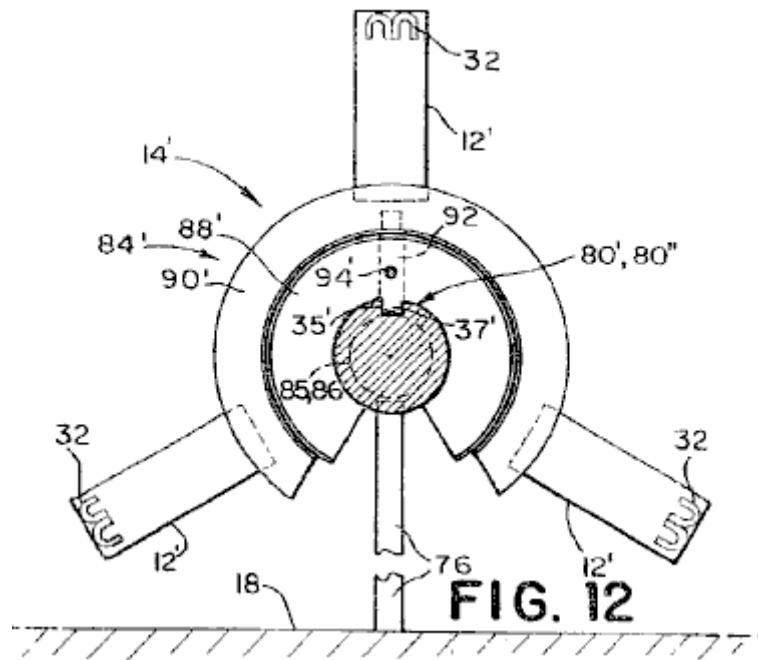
es un final elevational la vista de la asamblea de rotor mostrada en Fig.11B, adelante incluso un poste de montaje ferroviario;
